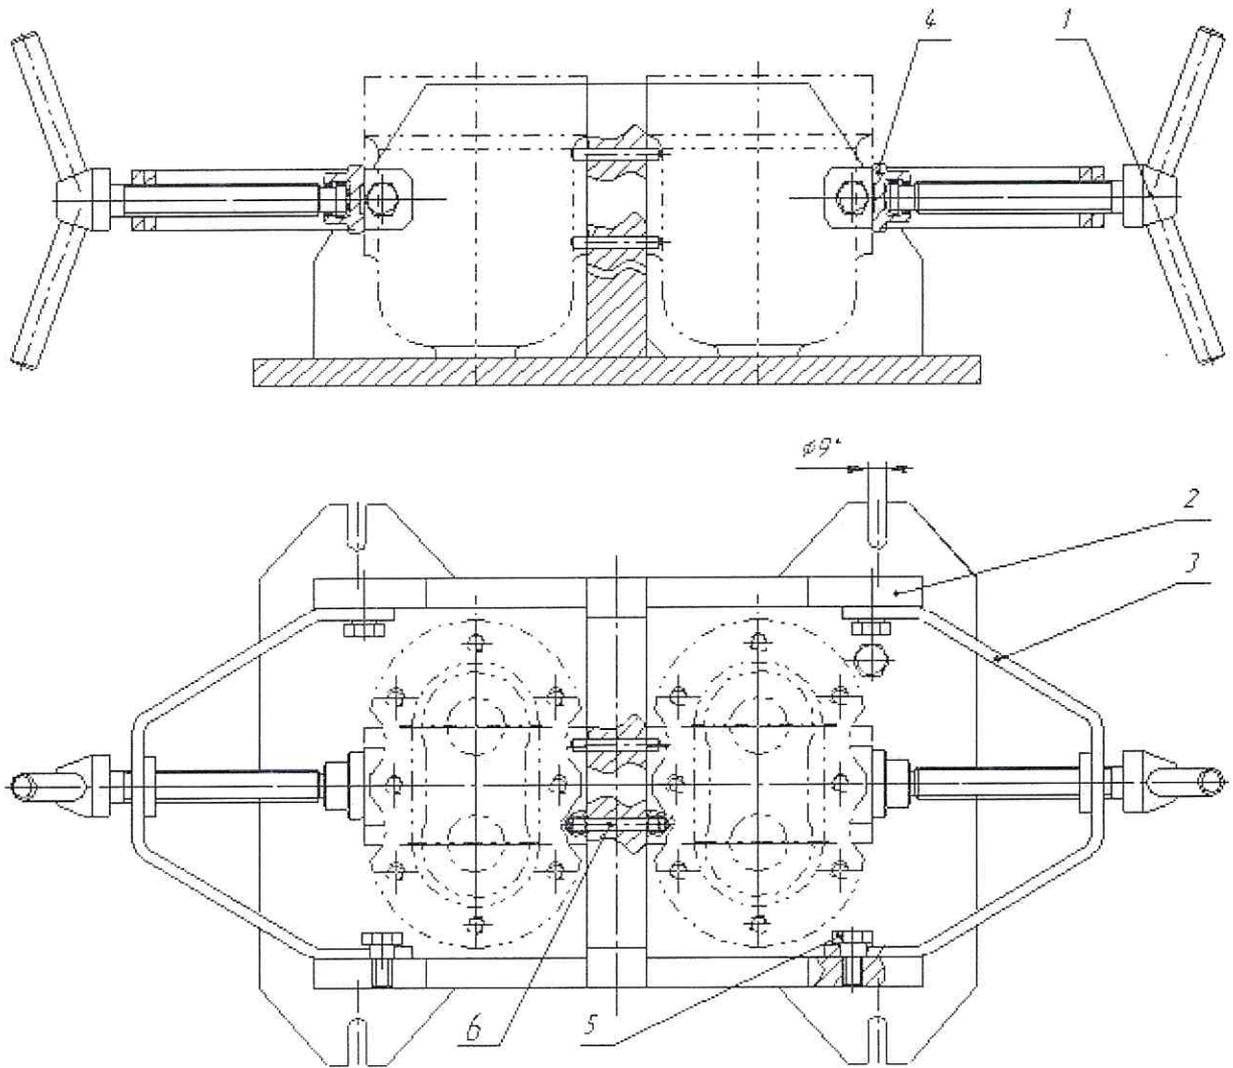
Предлагаемое приспособление для обработки корпуса гидронасоса на фрезерном станке
